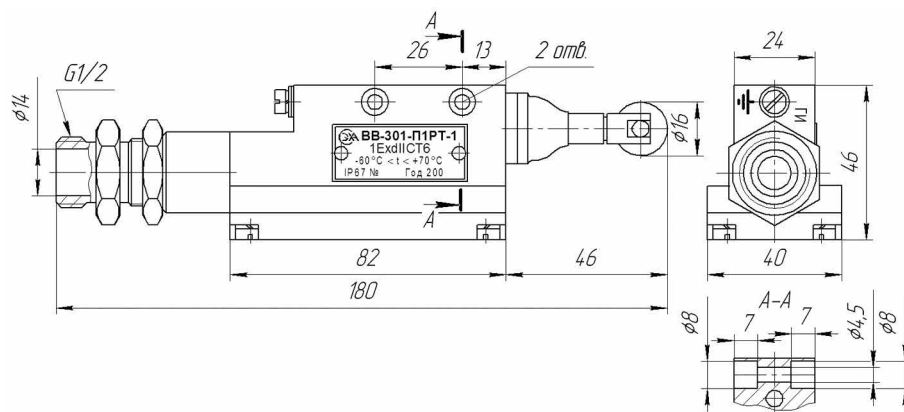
Габаритные и установочные размеры ВВ-301-П1РТ-1
